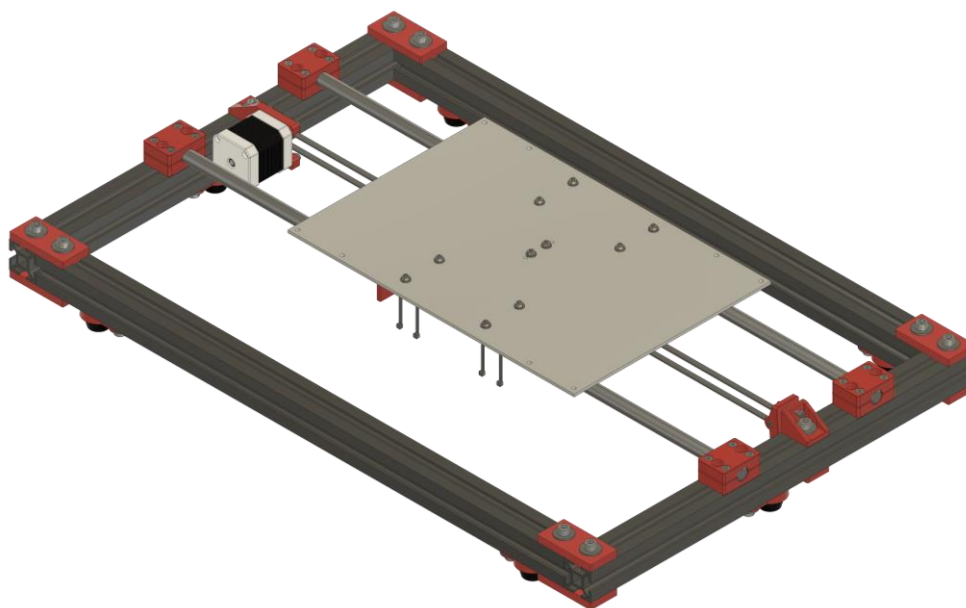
Stolek osy Y s držáky lineárních ložisek
